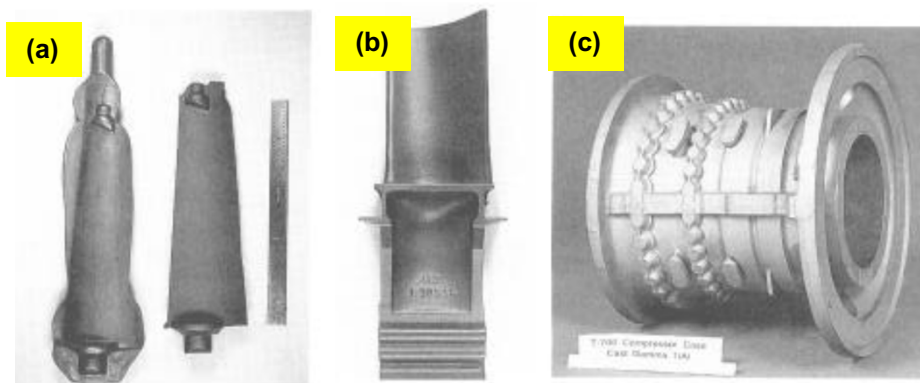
(a) profilo alare α_2 forging, (b) paletta di turbina al primo stadio γ casting, (c) case del compressore γ casting [16]
